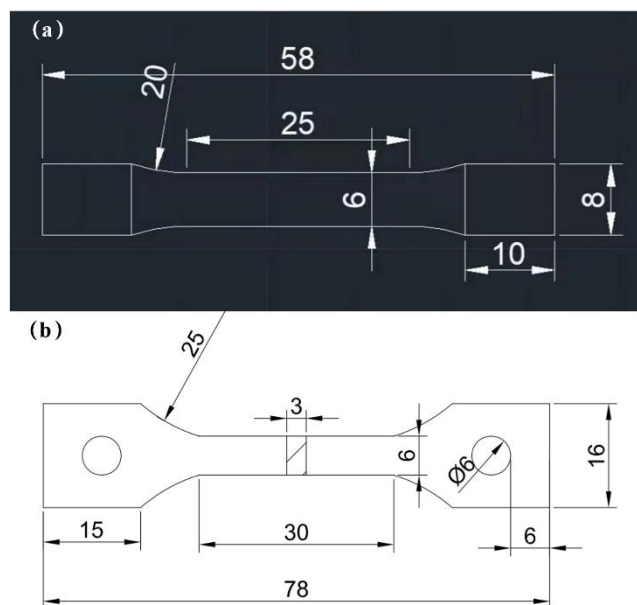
拉伸尺寸 (a) 室温拉伸尺寸 (b) 高温拉伸尺寸
